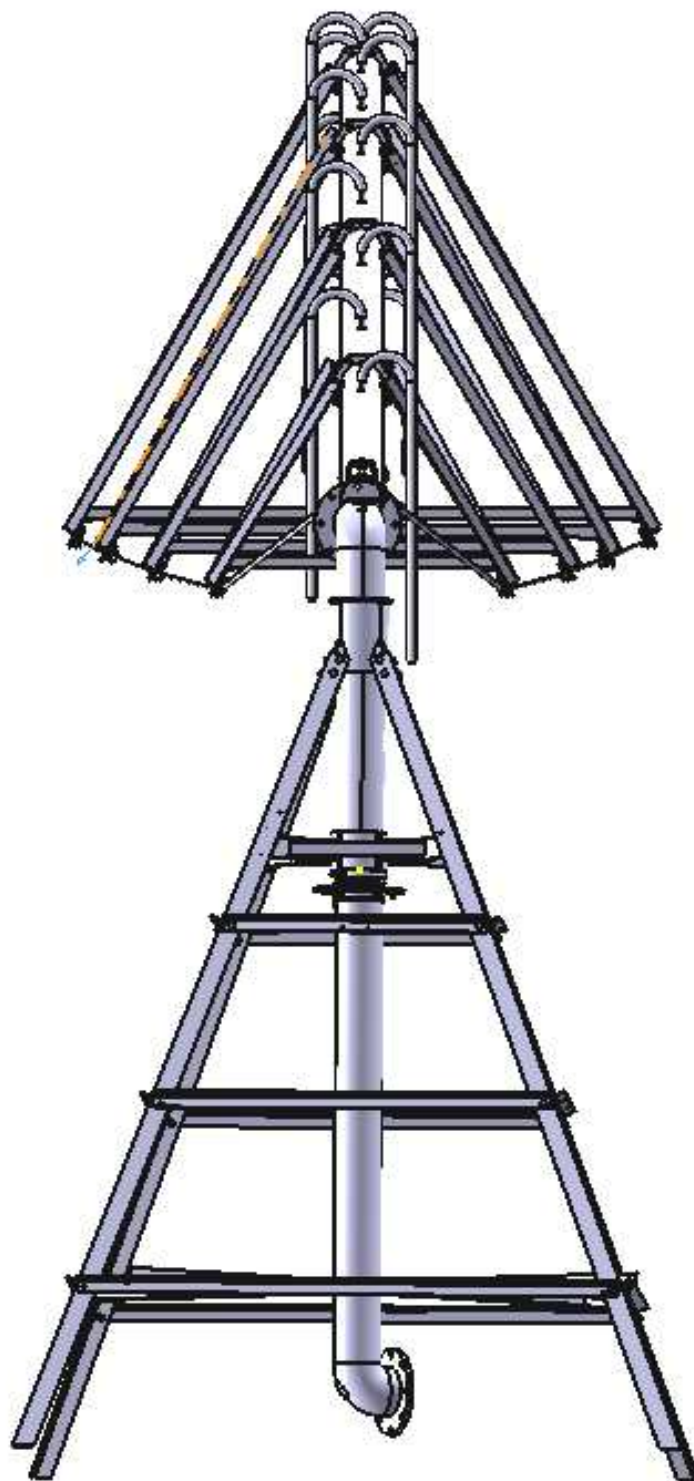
Assemblage de la travée à la tour centrale (vue de face)
